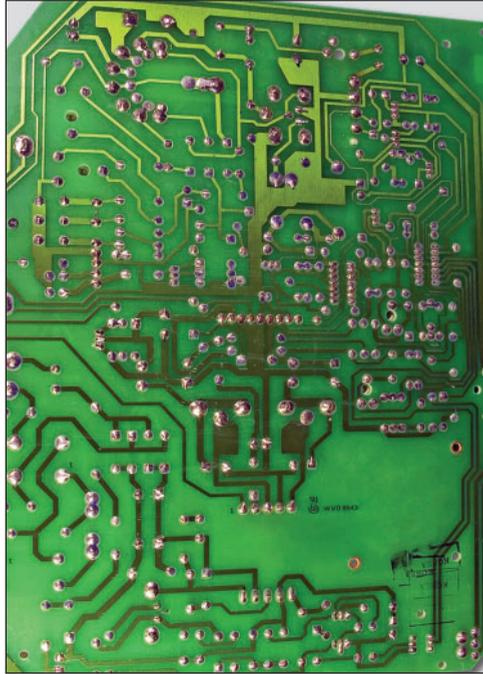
Reverso de la placa de una fuente de energía. Retirla de la carcasa nos permitirá medir y desoldar componentes con mayor comodidad.
